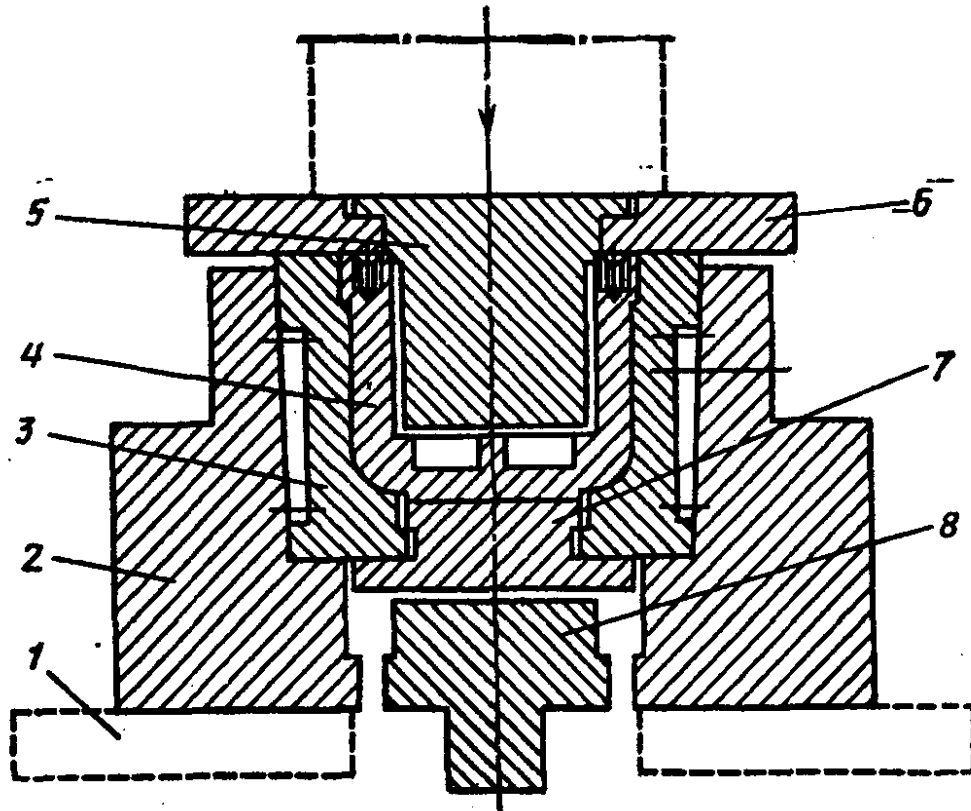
Схема гарячого пластичного деформування корпусу шестеренного насоса:
